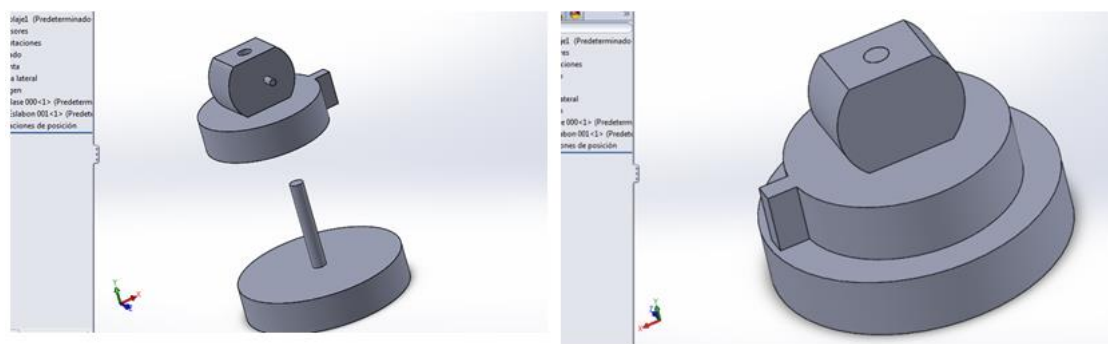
Izquierda: ensamble de parte fija y cintura, Derecha: Ensamble con movimiento
